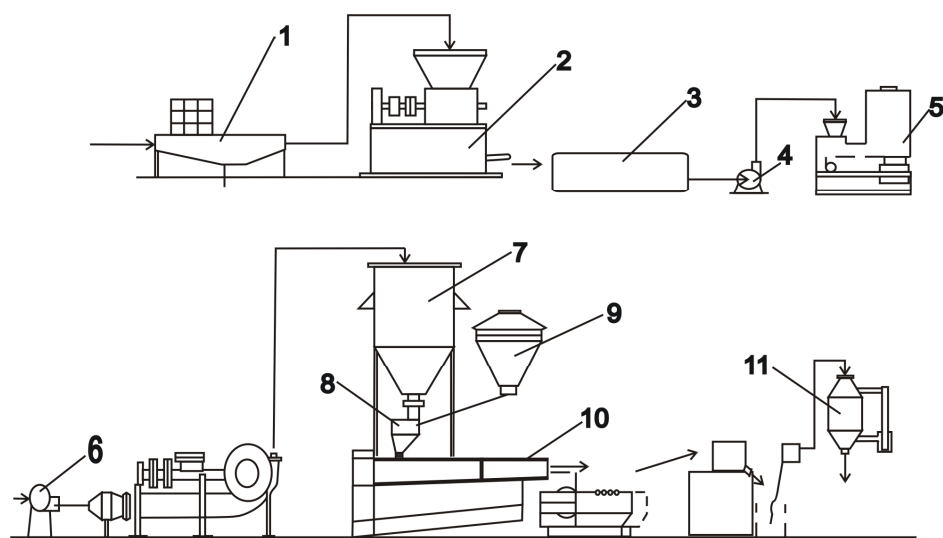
Технологическая схема: 1 – стол разборки сырья; 2 – установка для предварительного измельчения пленки; 3 – ванна; 4 – пневмотранспорт; 5 – установка для непрерывной отмывки; 6 – вихревая сушилка; 7, 9 – бункер; 8 – питатель дозатор; 10 – линия гранулирования вторичных термопластов; 11 – сушилка гранулята
